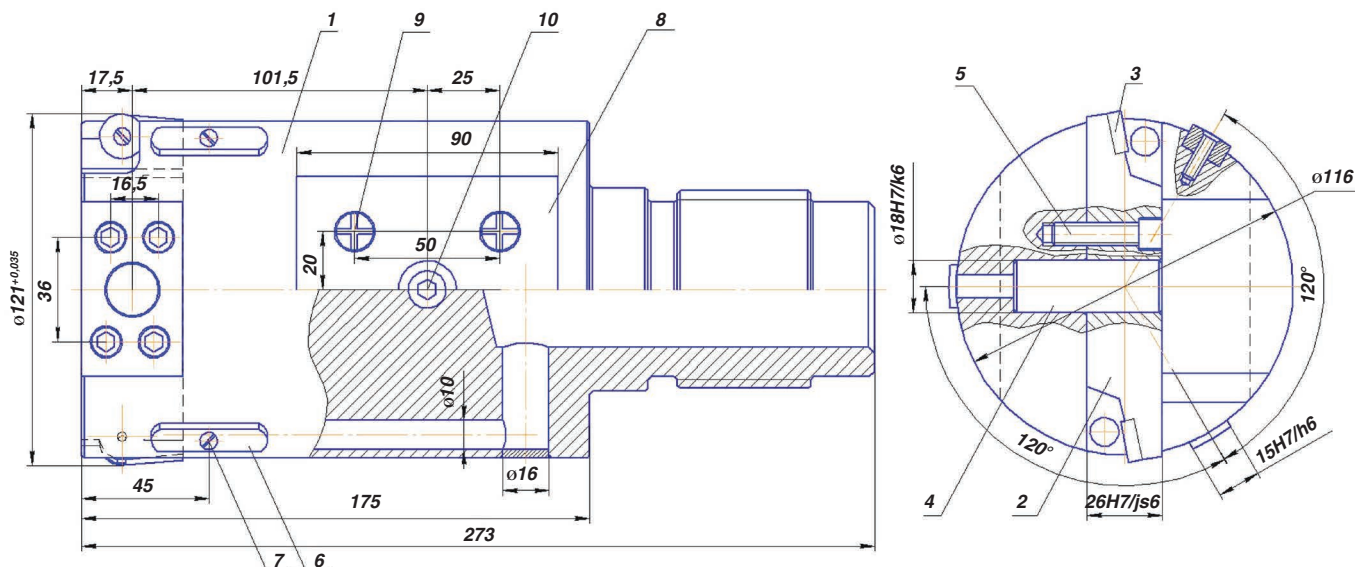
Эскиз расточной головки для обработки глубоких отверстий в деталях типа тел вращения.
